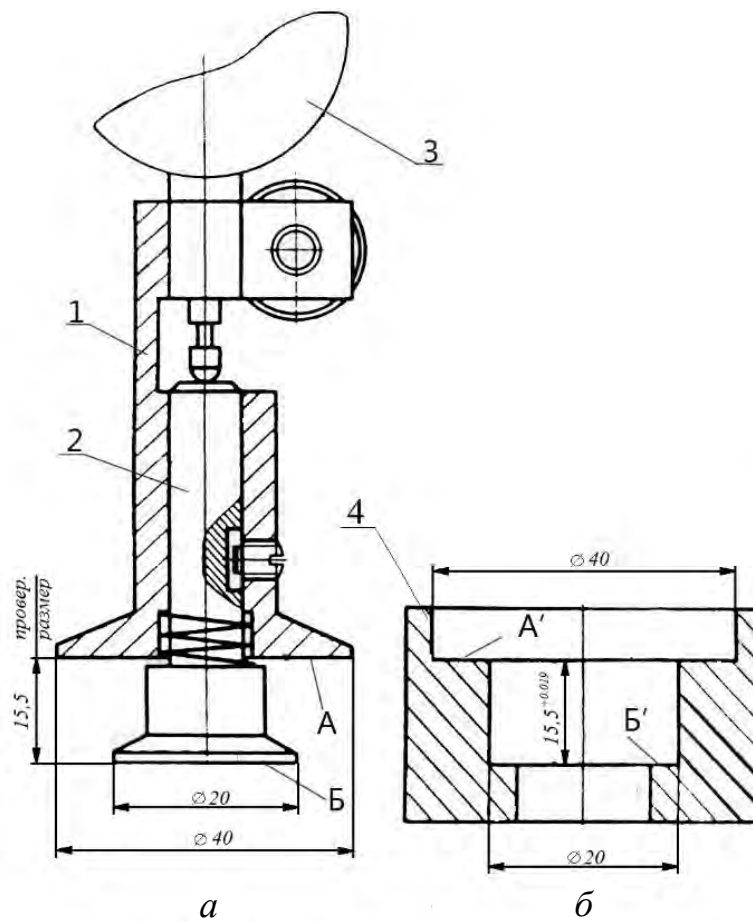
Переналаживаемое приспособление для контроля линейных размеров оправы
